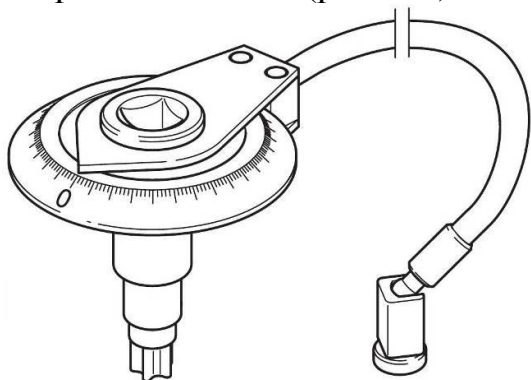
Приспособление для регулировки теплового зазора двигателей DEUTZ
